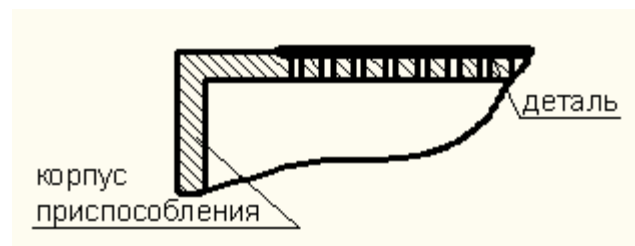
Схема закрепления легко деформируемых заготовок.
